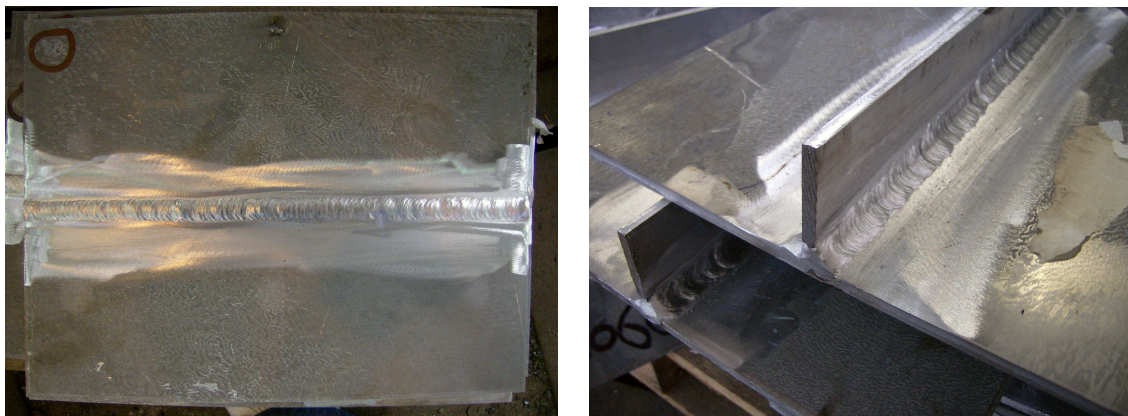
Provetes soldados topo a topo e provete soldado com junta em T.
